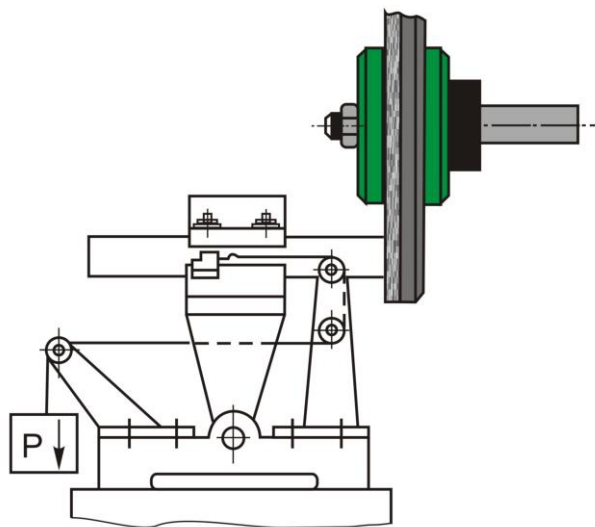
Общий вид приспособления для исследования режущей способности боковых поверхностей отрезных кругов
